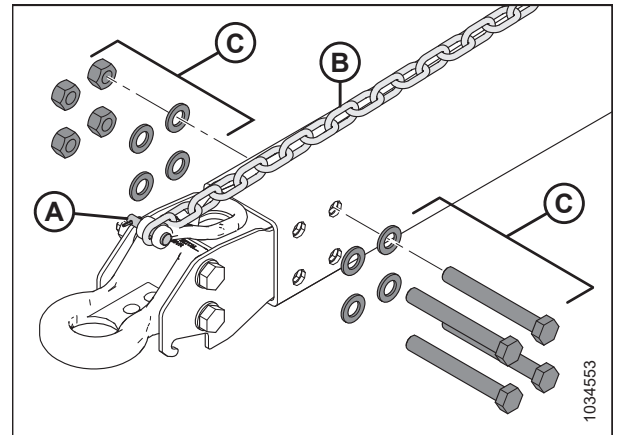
Знімання адаптера зчіпного пристрою для буксирування
